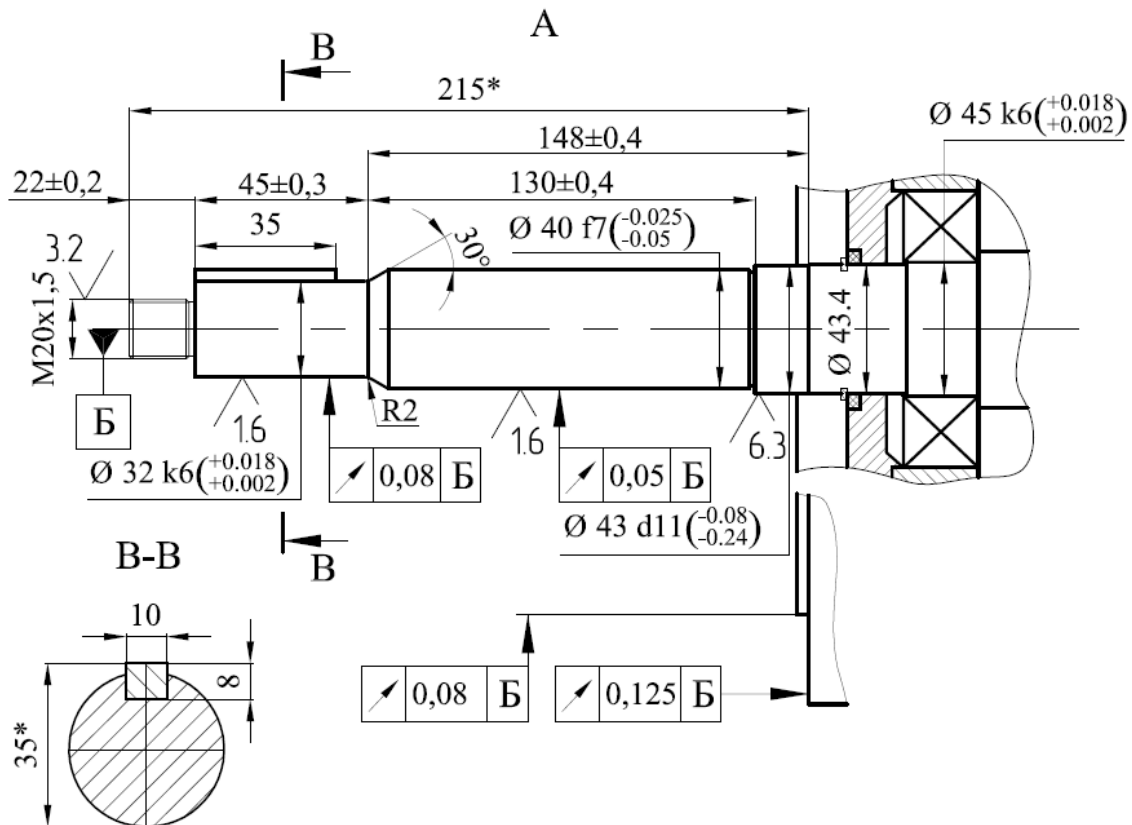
Свободный конец вала двигателя 6АМУ160S2ЖУ2
